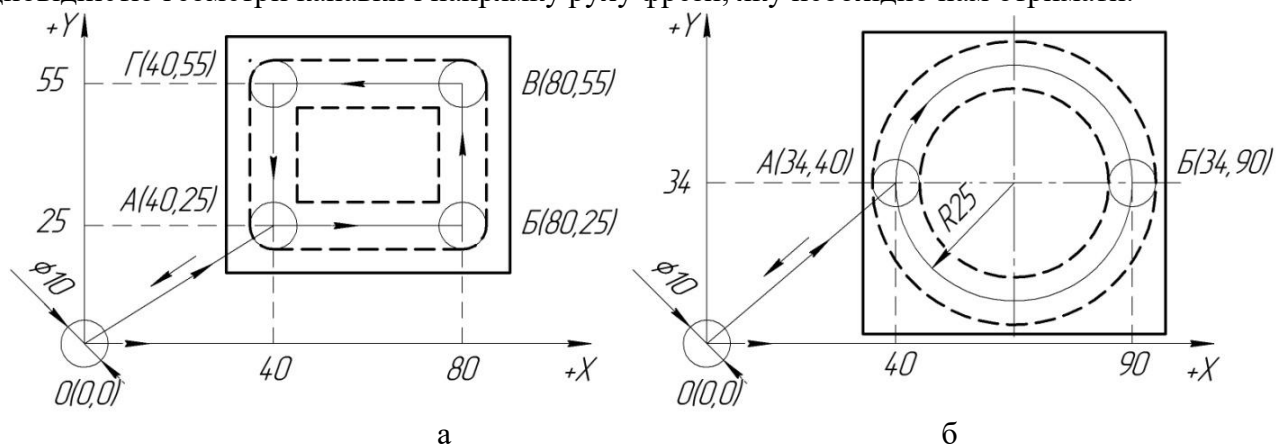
Фрезерування канавки по прямій (а) і по колу (б)
